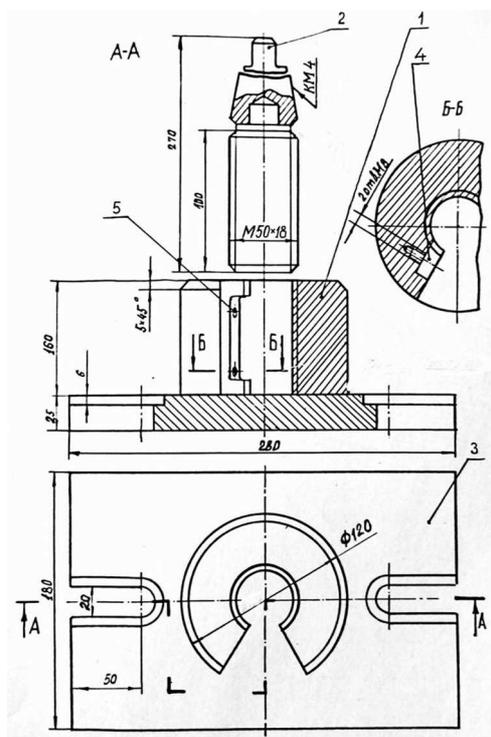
Пресс для выдавливания профиля резьбы на свинцовых образцах
